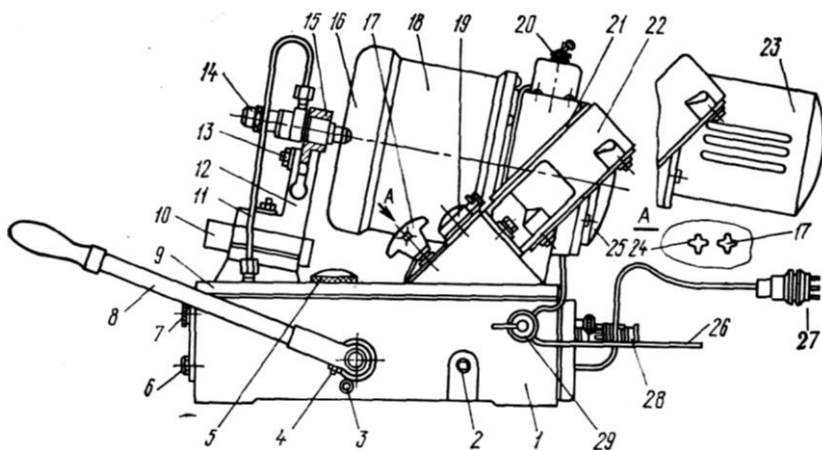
Прибор КИ-3333 для испытания и регулировки форсунок:
